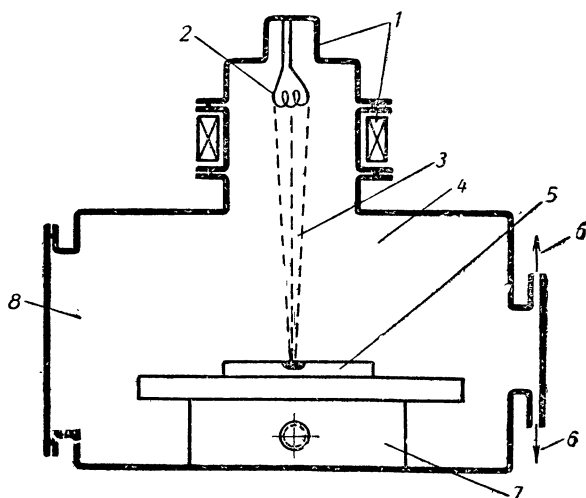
Схема сварки электронным лучом: 1 — электронная пушка; 2 — катод; 3 — пучок электронов; 4 — вакуумная камера; 5 — обрабатываемая деталь; 6 — к вакуумным насосам; 7 — механизм перемещения детали; 8 — загрузочное и смотровое окно.
